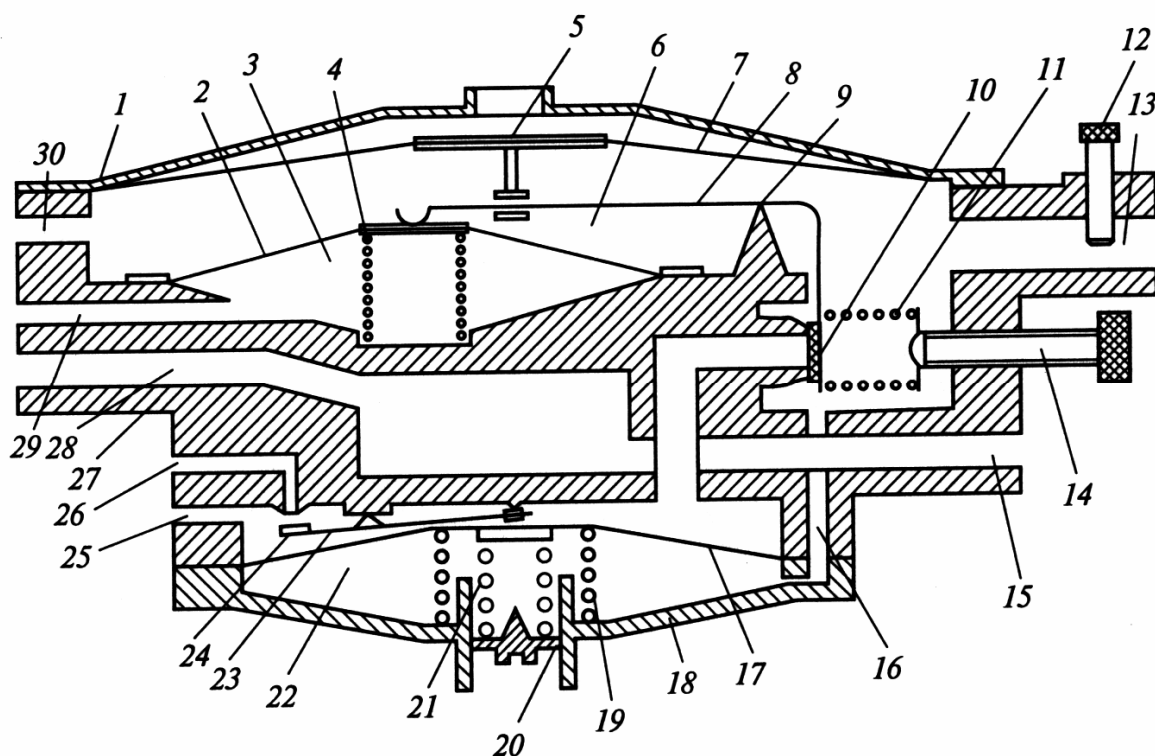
Схема редуктора-испарителя низкого давления НПФ «САГА»:
